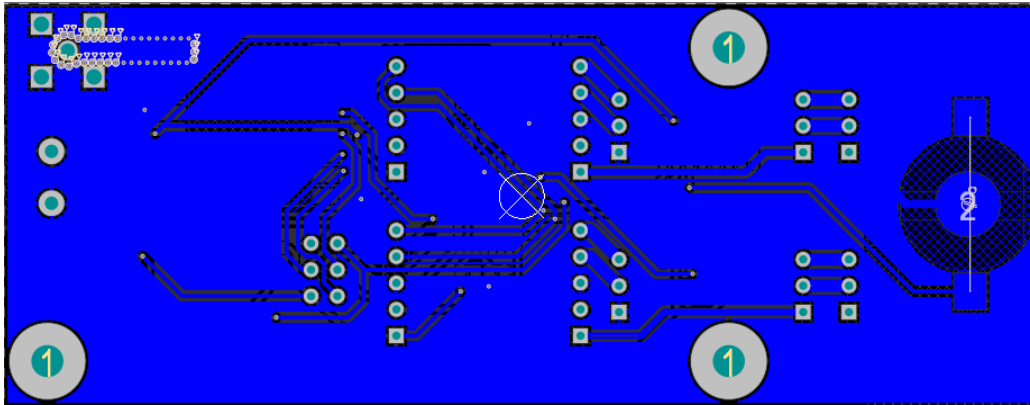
30 Diseño PCB, capa inferior (Bottom Layer)
